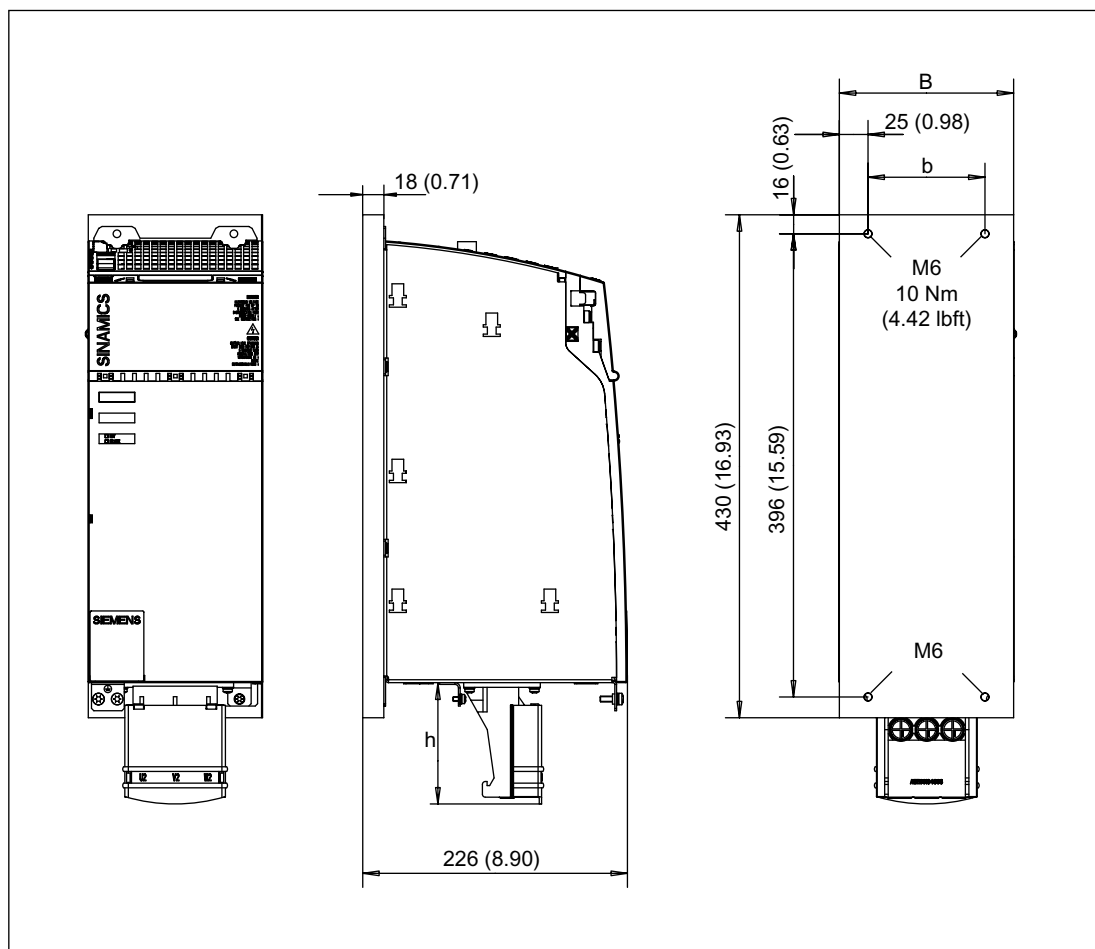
Disegno quotato Motor Module con Cold-Plate 60 A e 85 A
